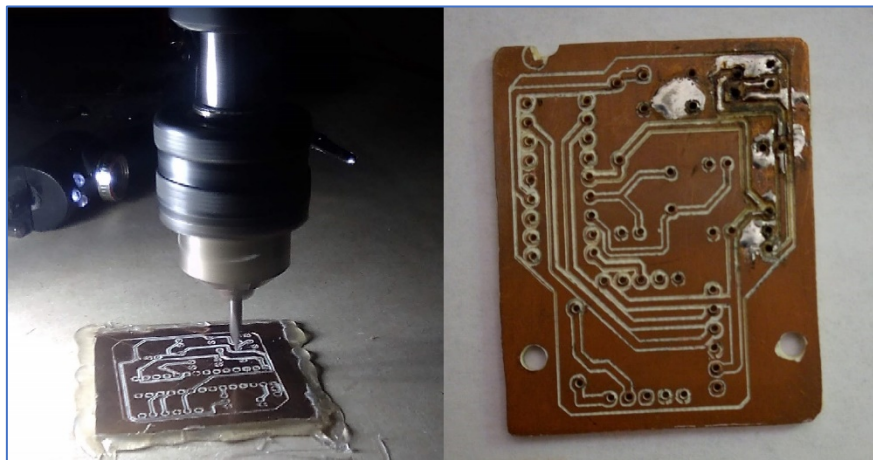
Izquierda) Maquinado de placa; Derecha) Placa generada
